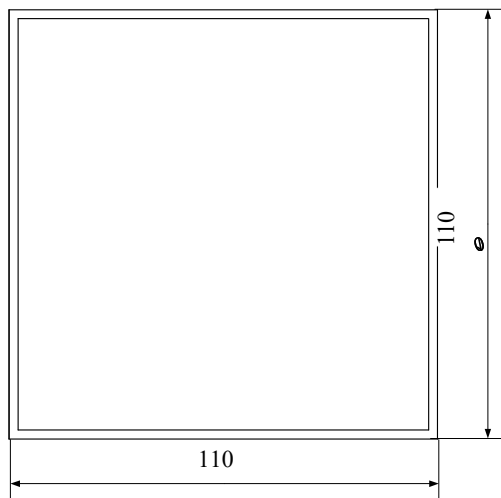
Габаритный чертеж ПЛК серии MC. Вид спереди.
